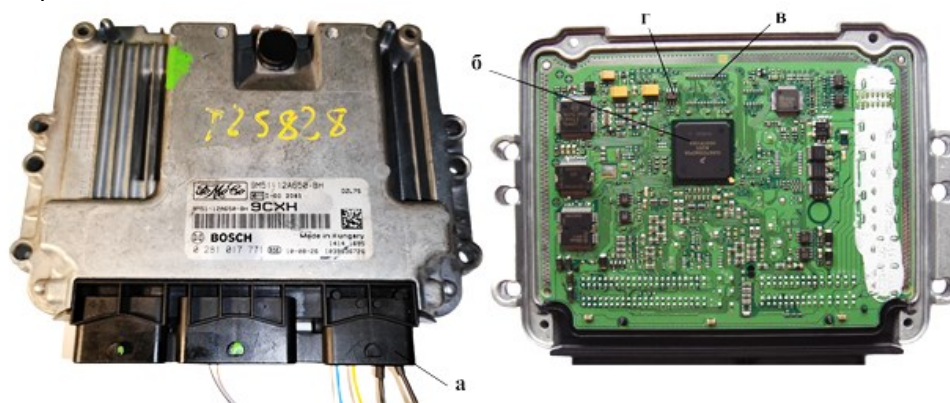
Общий вид и фото платы ЭБУ EDC16C34:
